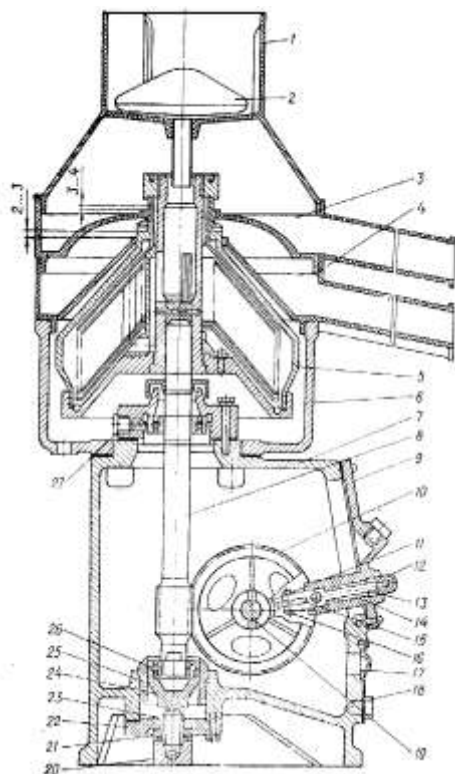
Сепаратор сливокідокремлювач ОСБ: 1 – поплавкова камера; 2 – поплавок; 3 – прийомник для сливок; 4 – прийомник для обезжиреного молока; 5 – барабан; 6 – чаша станини; 7 – станина; 8 – вертикальний вал; 9 – кришка; 10 – черв’ячна шестерня пульсатора; 11 – шестерня пульсатора; 12 – ковпачок пульсатора; 13 – шток пульсатора; 14 – пружина пульсатора; 15 – ексцентрична шестерня пульсатора; 16 – вісь ексцентричної шестерні; 17 – показчик рівня масла; 18 – пробка; 19 – горизонтальний вал; 20 – контргайка; 21 – контргайка; 22 – кришка нижньої опори вертикального вала; 23 – гвинт підп’ятника; 24 – п’ята; 25 – стакан; 26 – радіально-упорний підшипник; 27 – пружна опора.
